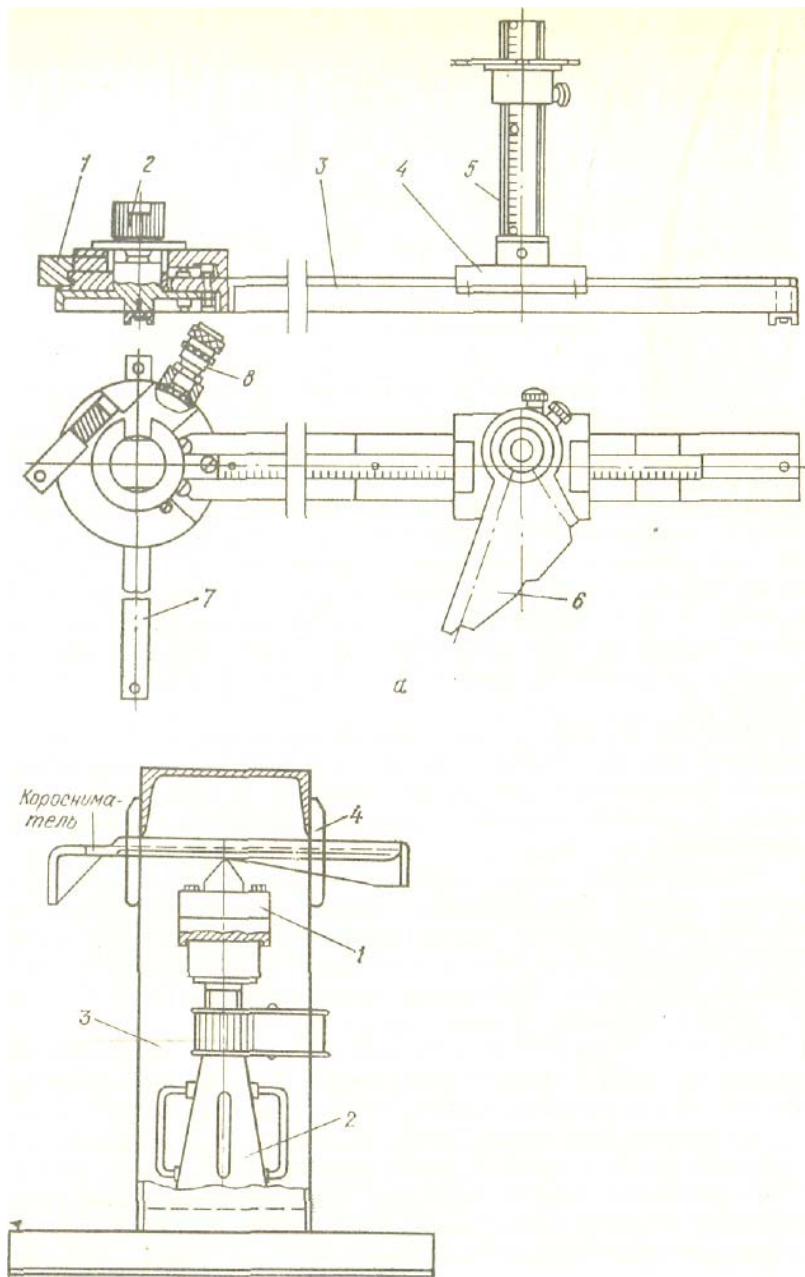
Приспособление для контроля и правки короснимателей: а – для контроля параметров; б – для правки.
